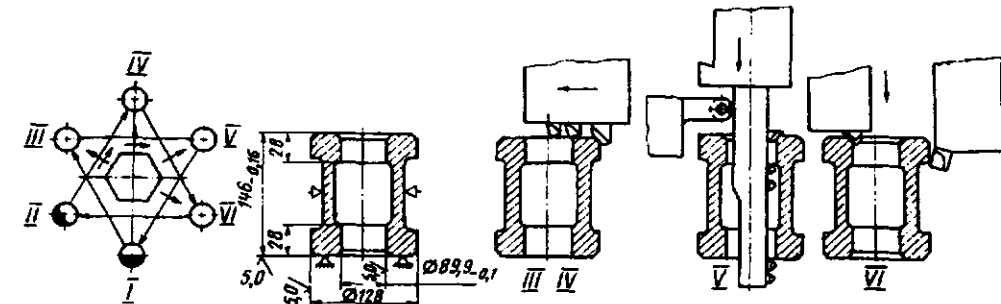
Наладка шестишпиндельного полуавтомата для двухциклового обработки корпусной детали с применением откидной борштанги
